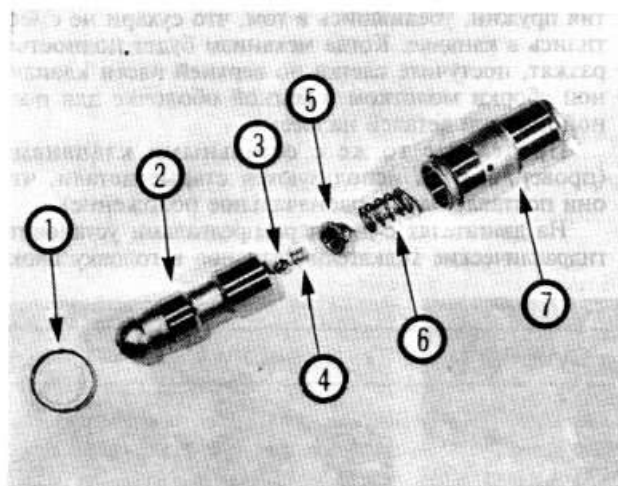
Детали гидравлических толкателей клапанов — двигатель с одним распредвалом
